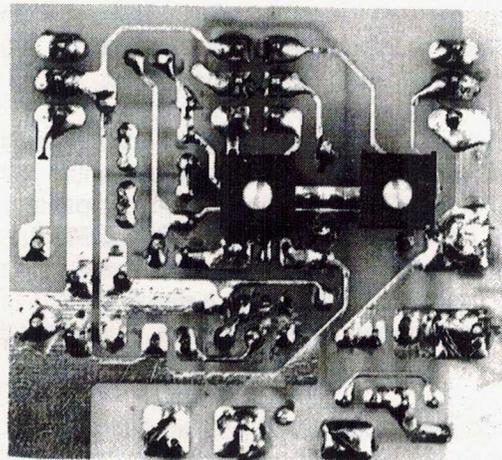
Foto del montaje visto desde el lado de los dos trimmer. Si se realizan soldaduras perfectas el circuito funcionará en cuanto lo hayáis terminado y ajustado.
